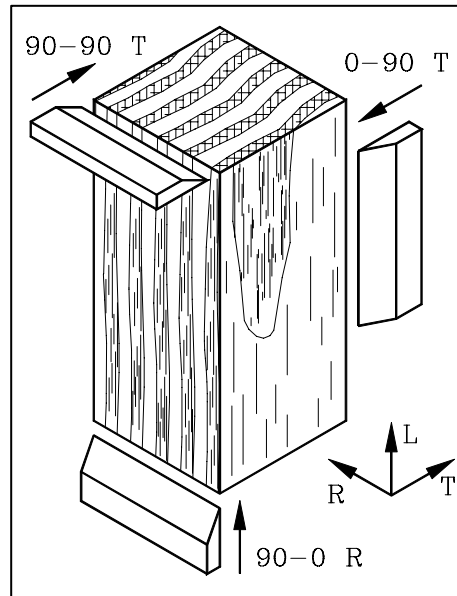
Modes fondamentaux de coupe du bois
